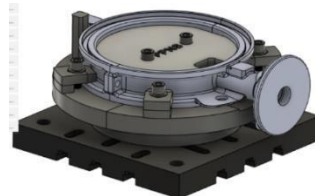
Konsep Desain 2 Jig dan Fixture Full Assembly
